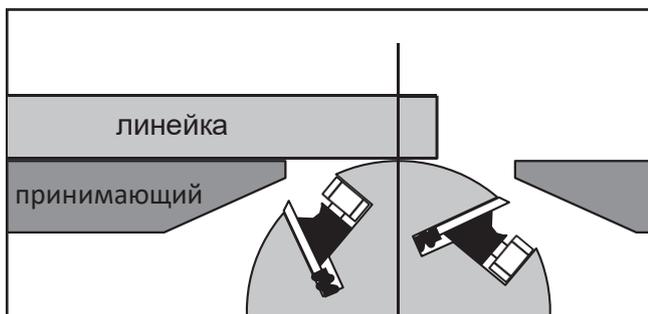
Регулировка отводящего стола с корпусом режущего вала.
